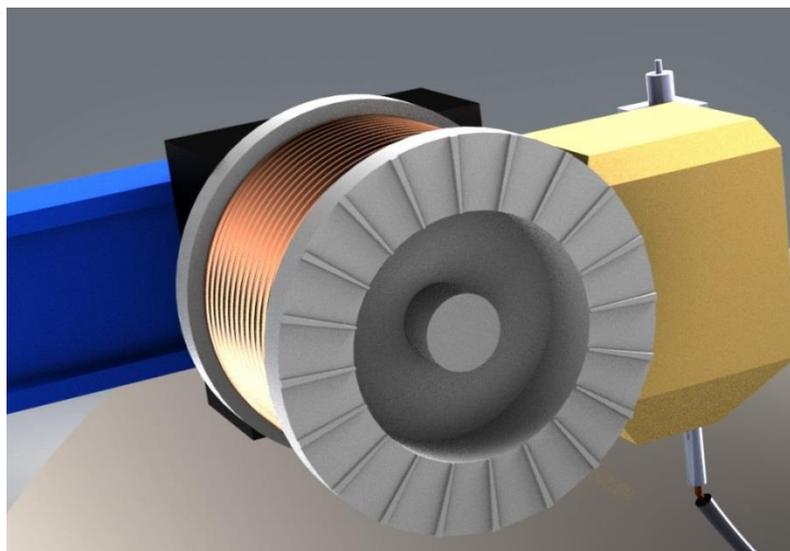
Автоматическая сварочная головка INMZ9
